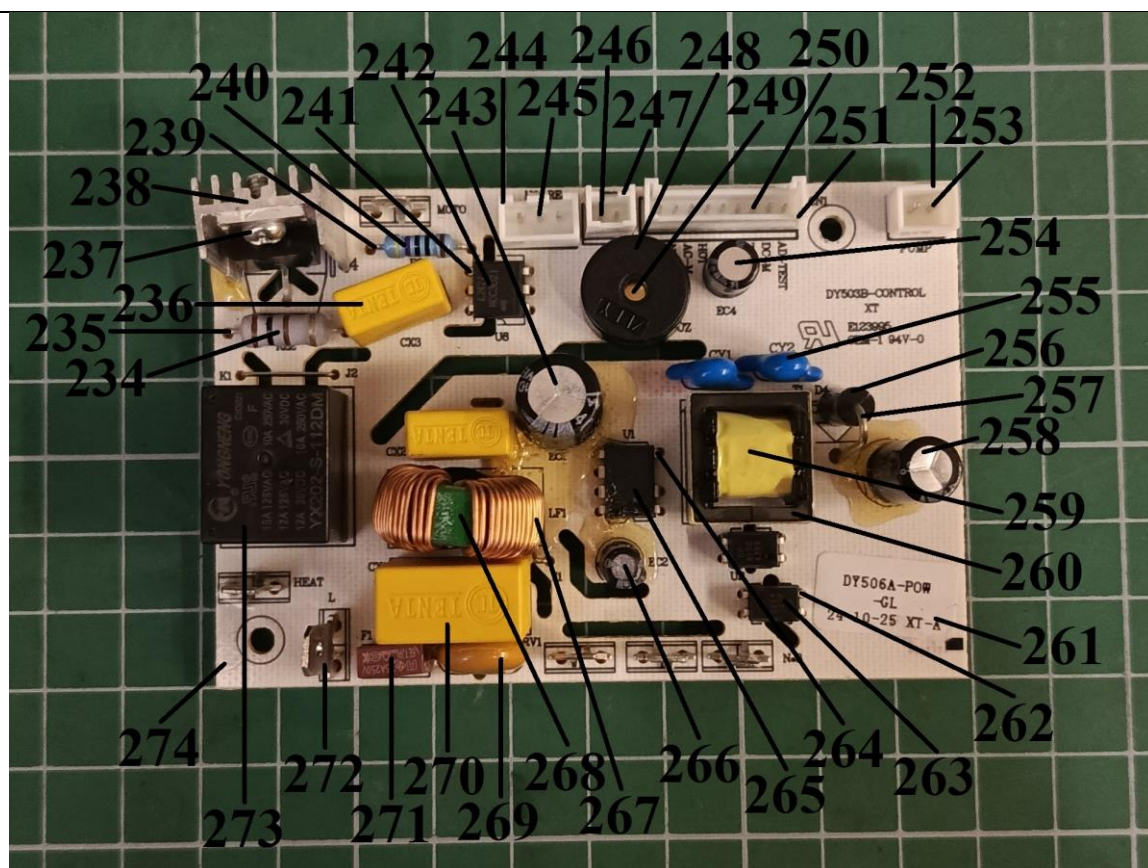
Элементы. Электрические приборы бытового назначения для чистки и уборки помещений: моющий пылесос, товарный знак Dumont, модель DMVC-3062.
